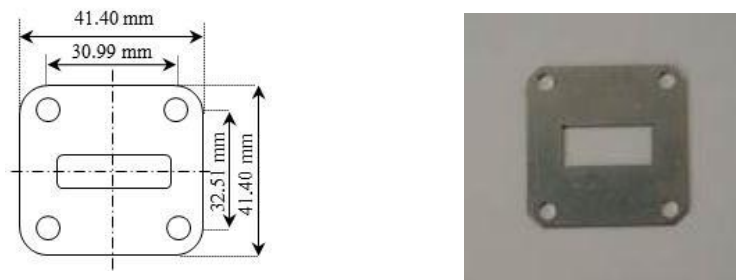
Plano con las dimensiones del molde (izquierda). Imagen del molde (derecha).
